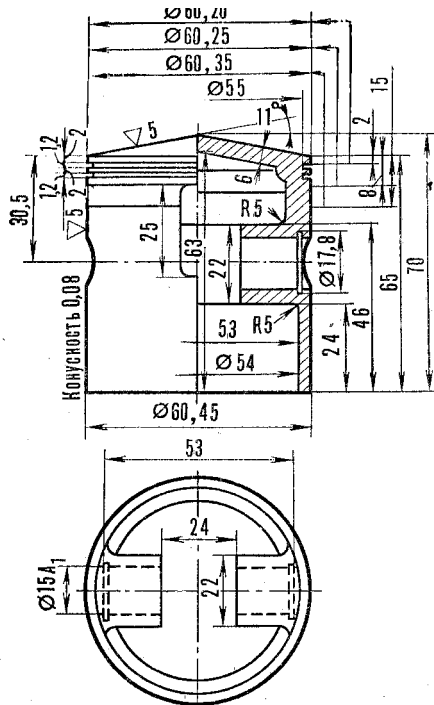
Поршень двигателя С-175 (материал АК-4). Длина юбки со стороны впуска 62 мм
